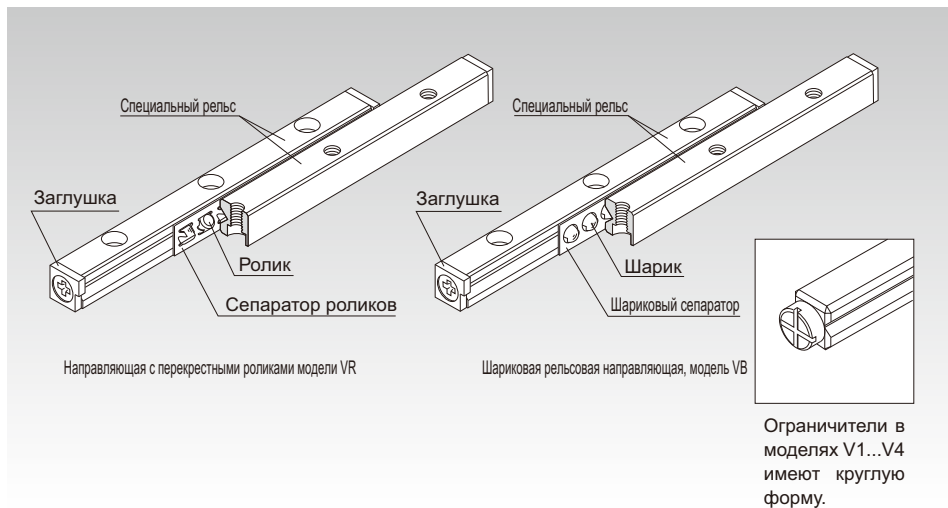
Конструкция направляющей с перекрестными роликами модели VB и шариковой рельсовой направляющей модели VB
